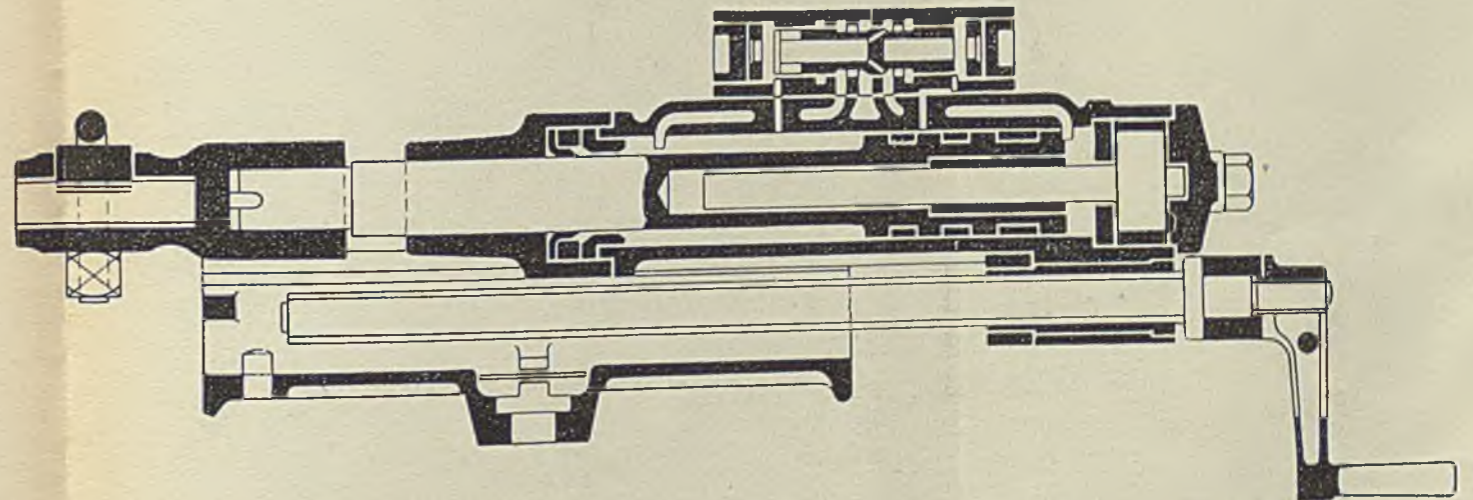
Gesteinsbohrmaschine (leichtes Modell) der Maschinenfabrik R. Meyer, Mülheim a. d. Ruhr.
